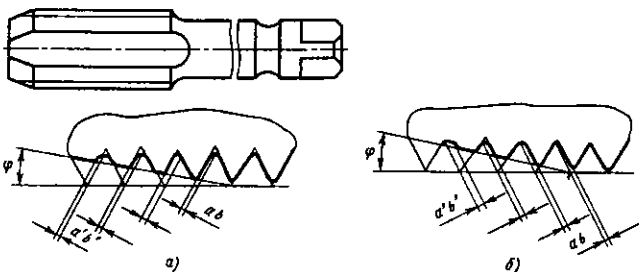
Метчики с режущими зубьями, зауженными со стороны хвостовика (а) и со стороны заборного конуса (б)
